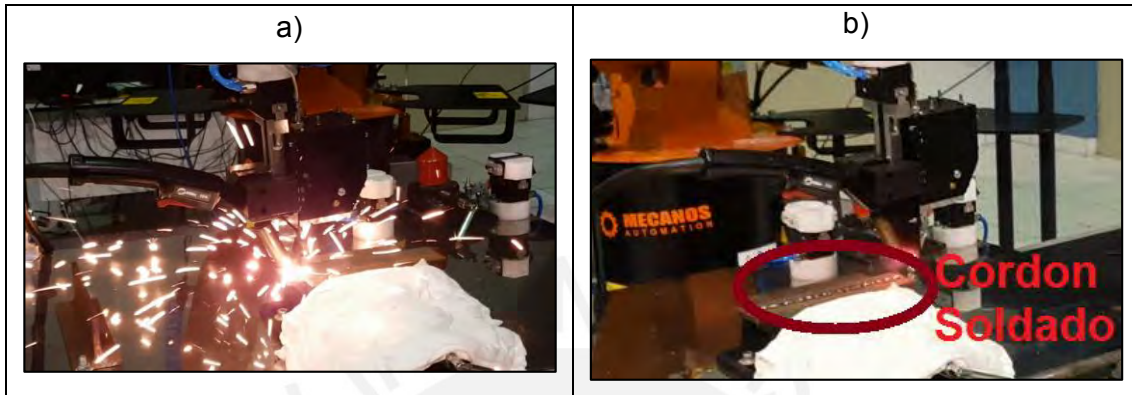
Validación de soldadura pre-programada, (a) durante la soldadura, (b) después de la soldadura
